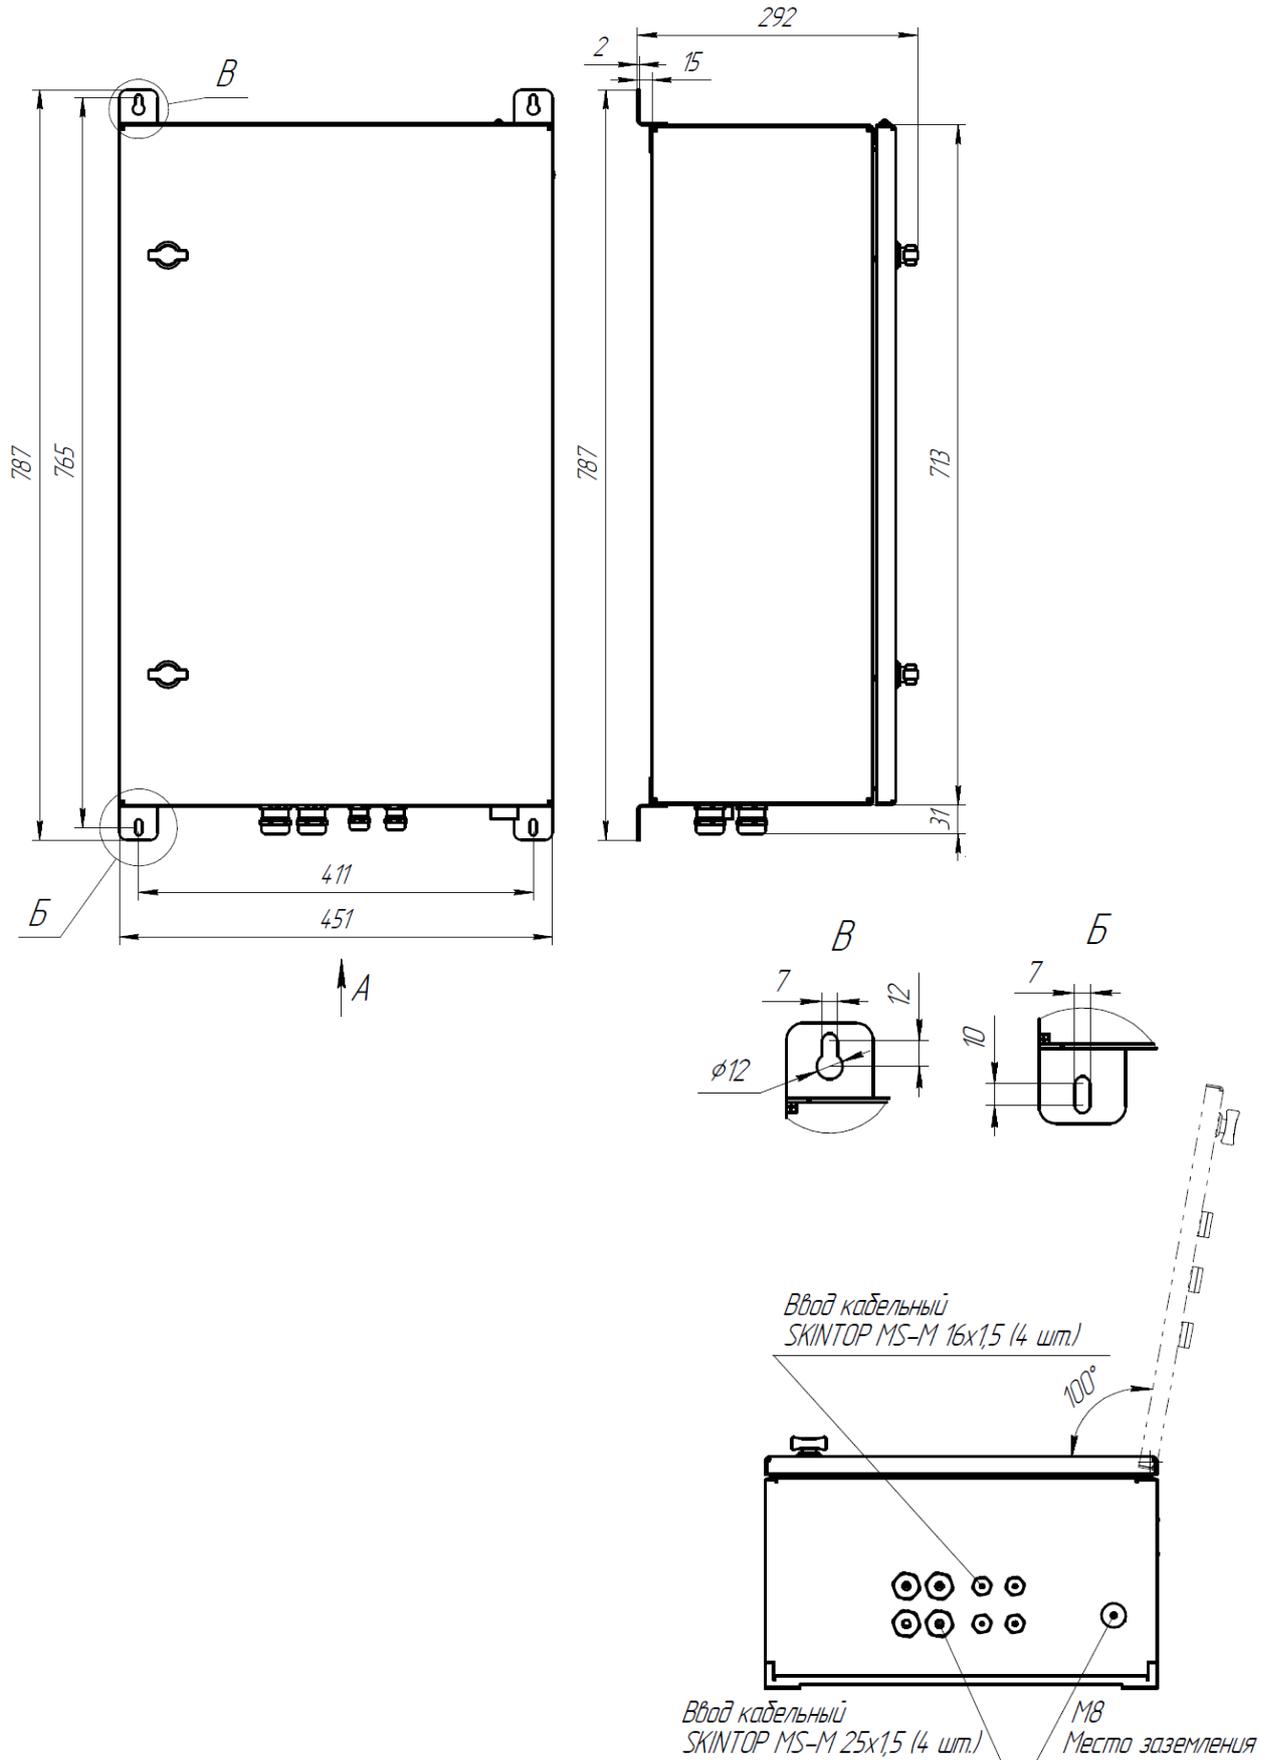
Габаритные и установочные размеры ЩПРМ
